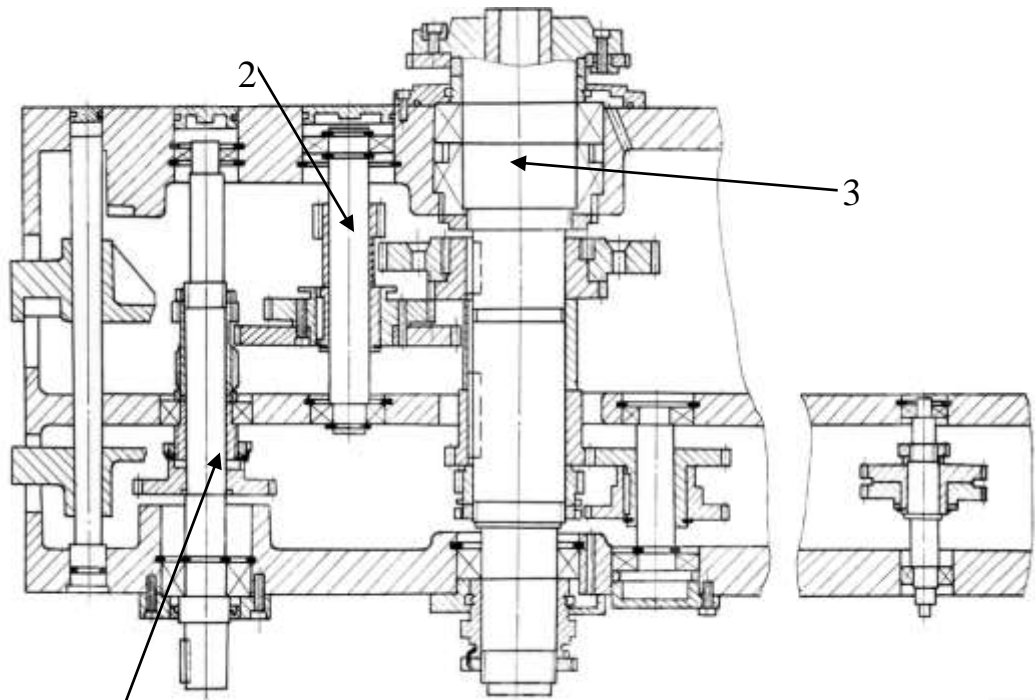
Шпиндельна бабка токарного верстата 16М30ФЗ
